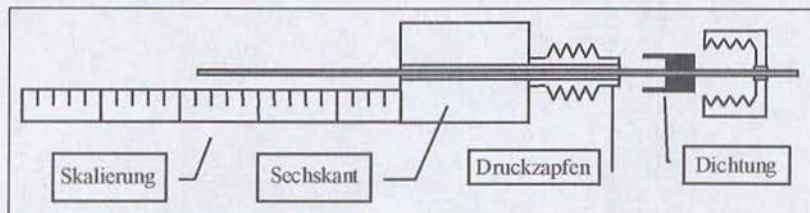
Montage der Dichtung auf die Kapillare mit Hilfswerkzeug.
